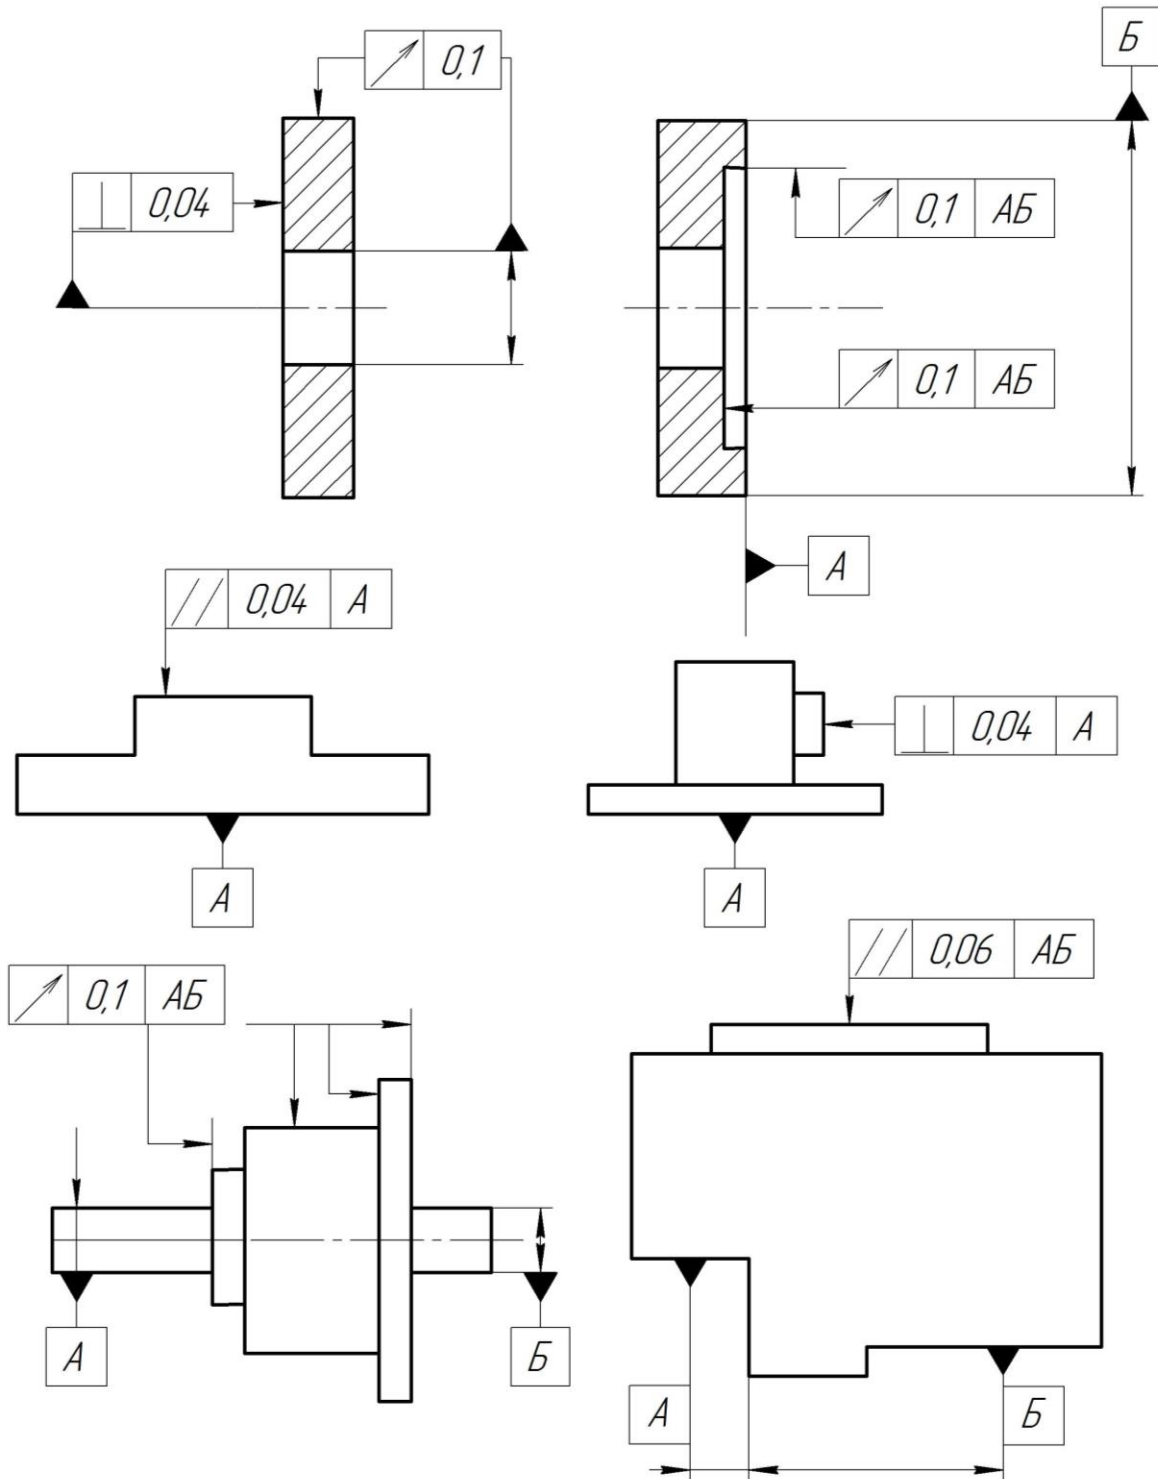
Приклади позначення на кресленнях допусків форми, розміщення поверхонь і баз
